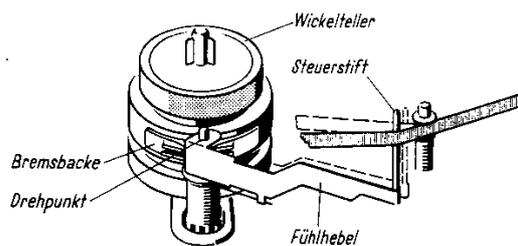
Bremsung des linken Wickeltellers mit einem Fühlhebel mit Steuerstift<sup>34</sup>
